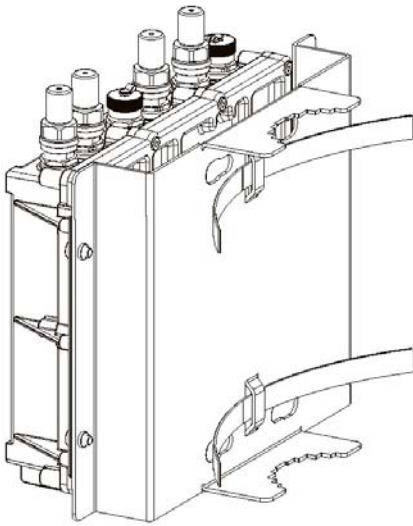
BAT450-F Masthalterungsset mit Spannbändern
